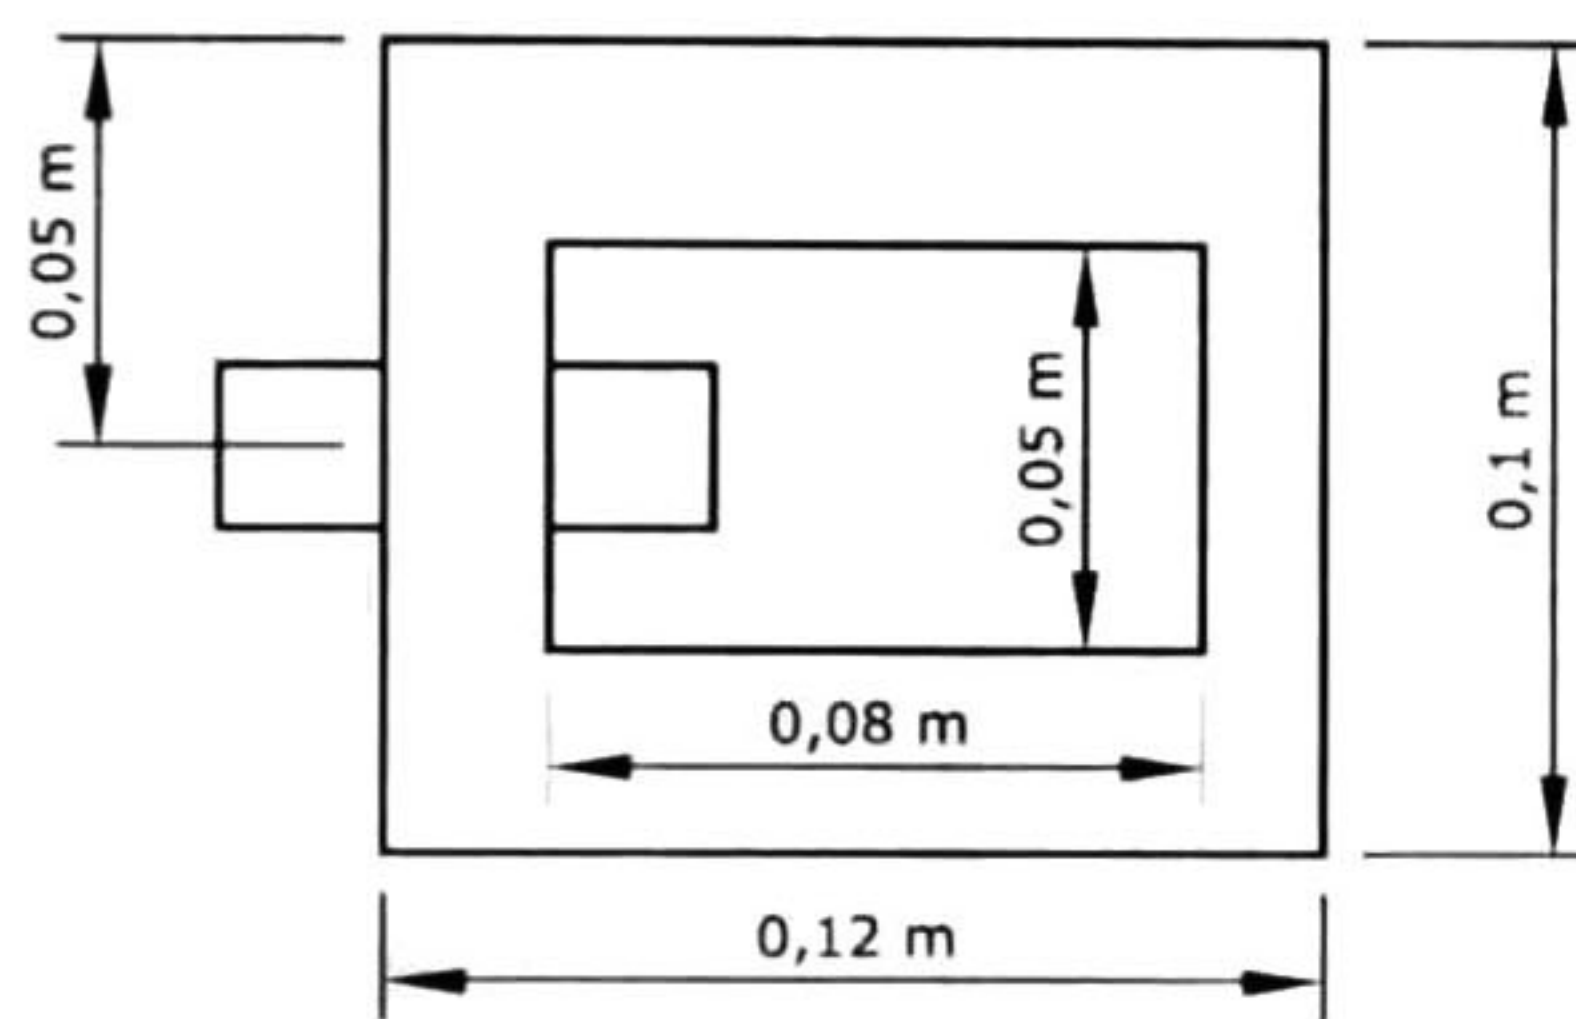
Dimensiones del núcleo del transformador monofásico.
